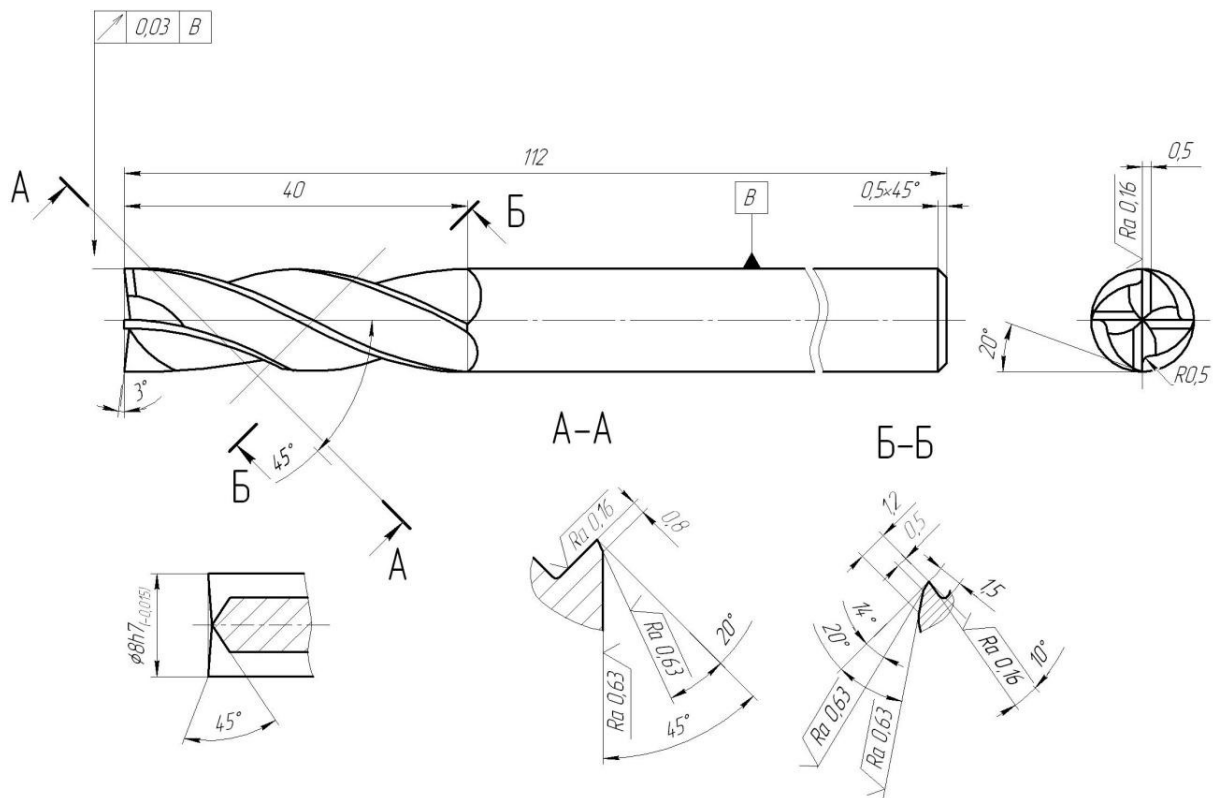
Креслення спроектованої кінцевої фрези
